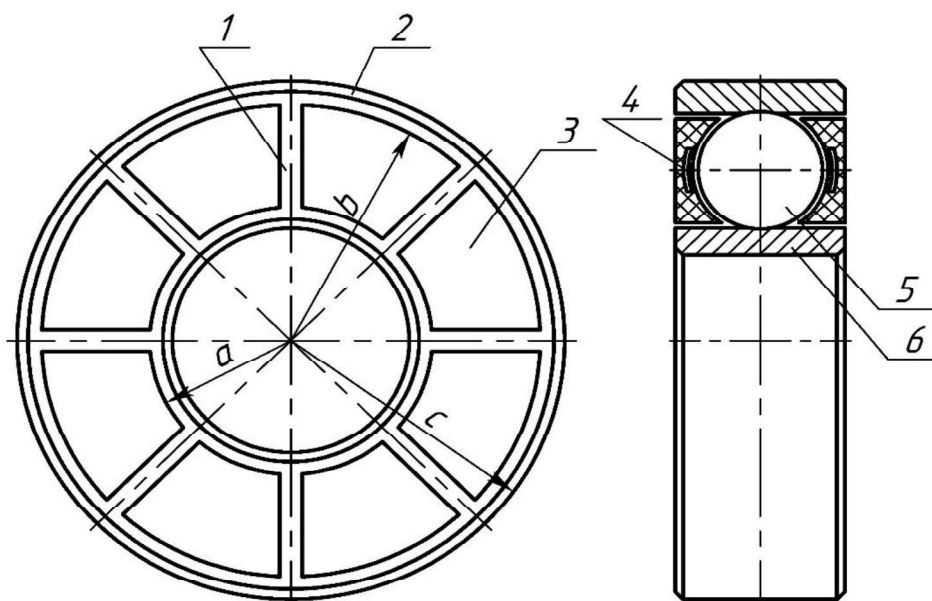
Подшипник с АФЗ с усовершенствованным наполнителем
